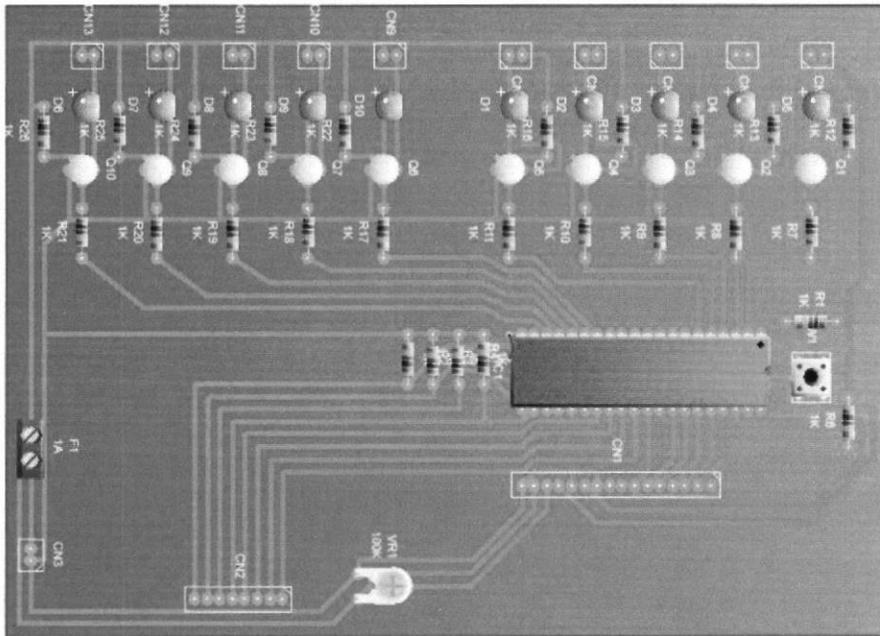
Circuito impreso en herramienta PCB Wizard.
